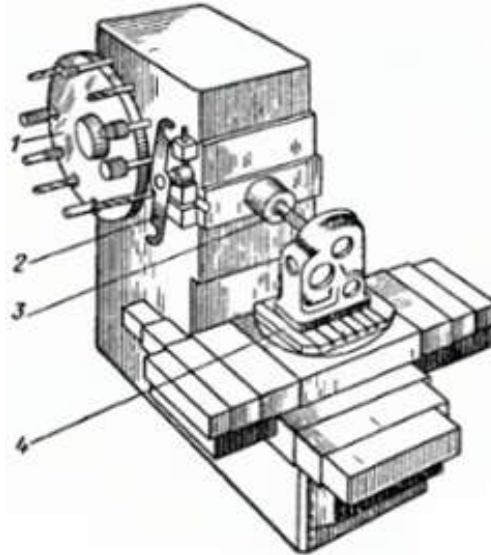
Компоновка горизонтального багатоопераційного верстата:
